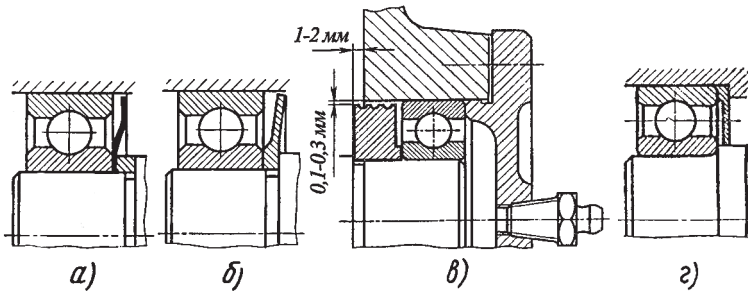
Внутренние уплотняющие устройства для подшипников:
